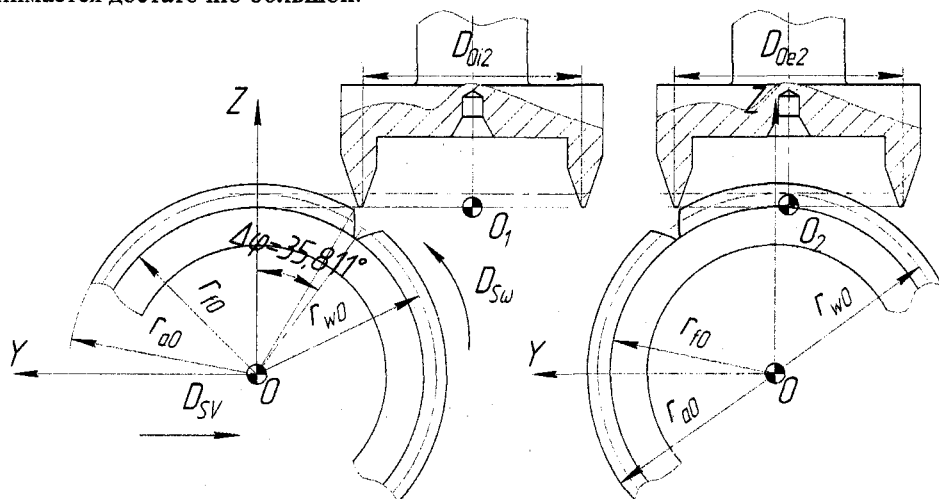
Движение обката при чистовой обработке выпуклой стороны зуба инструмента односторонней зуборезной резцовой головкой
